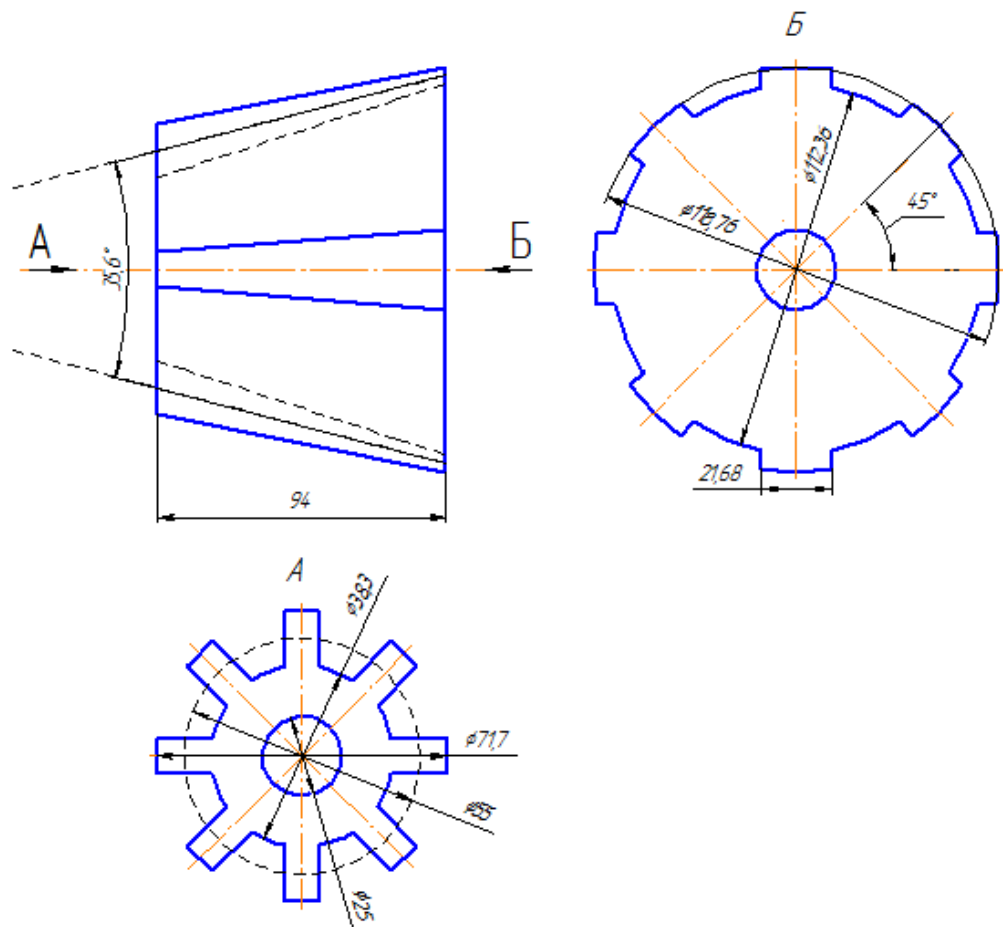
Схема формовочного вала (материал – Сталь 45)
